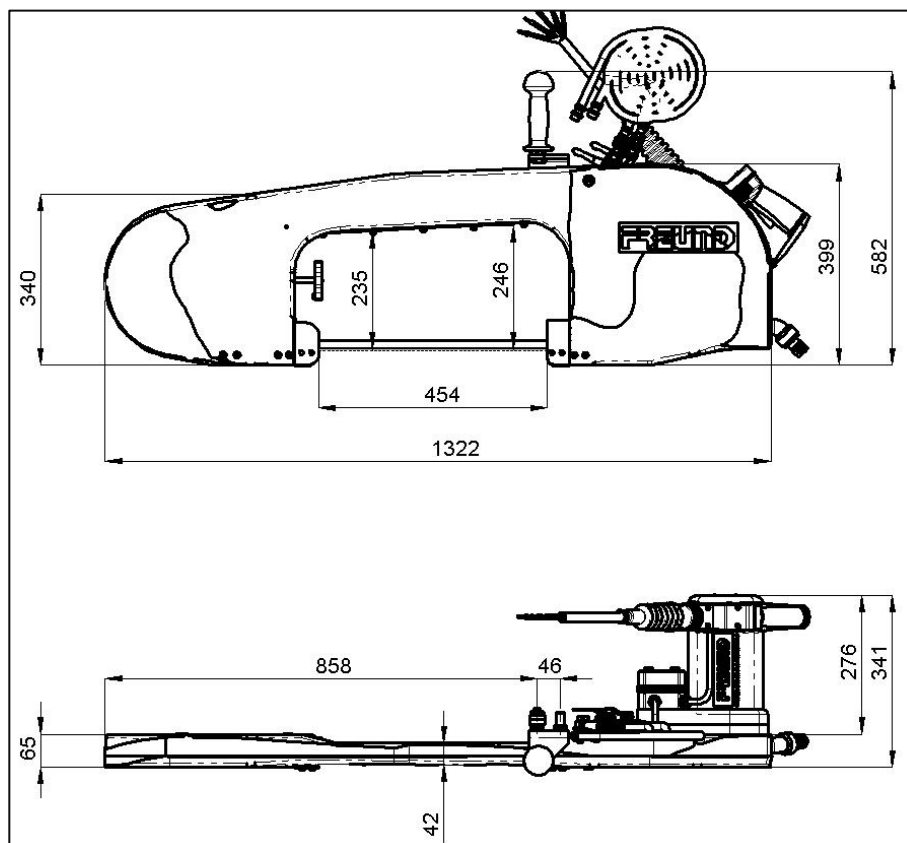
Widok standardowej piły SB46-08 szczegóły uchwytu – na górze po lewej piła standardowa, poniżej piła z załączaniem 2-ręcznym
